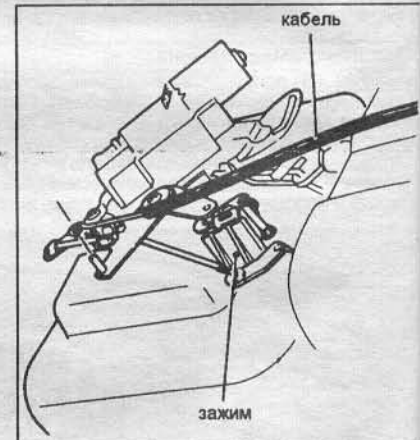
а Тяга смесителя воздуха обычно располагается с левой стороны корпус отопителя.
